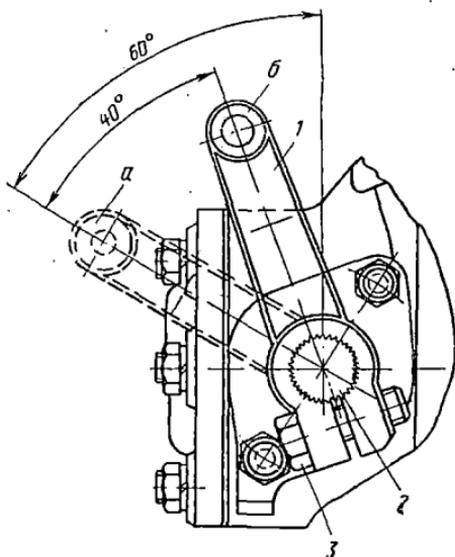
Регулировка муфты сцепления редуктора пускового двигателя тракторов Т-150, Т-150К: а — муфта включена; б — муфта выключена: 1 — рычаг включения муфты сцепления; 2 — валик рычага; 3 — стяжной болт
